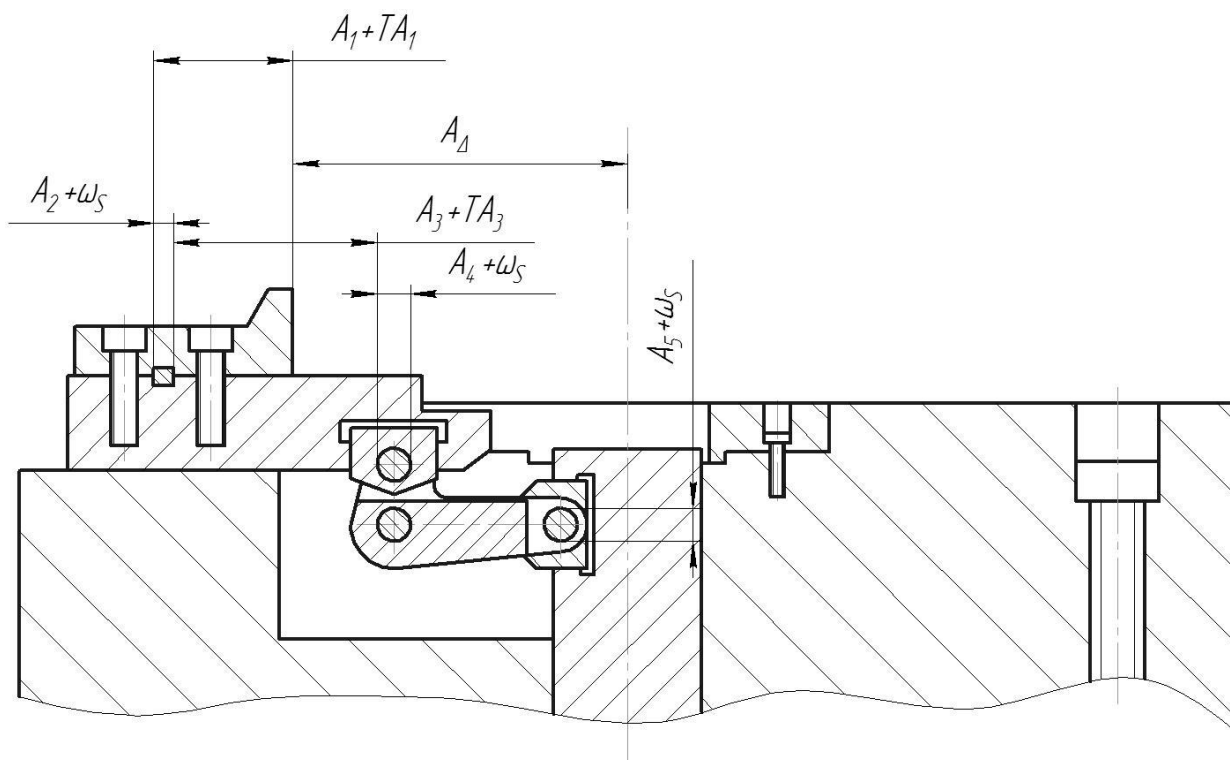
Расчетная размерная схемы погрешностей приспособления
